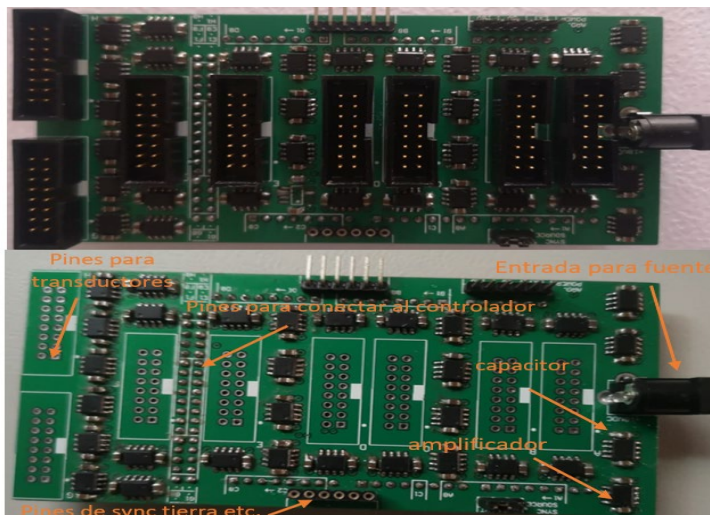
pcb terminada y pcb con descripción de los componentes soldados
